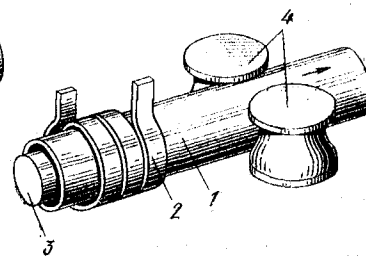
Схема сварки труб с индукционным подводом тока:
